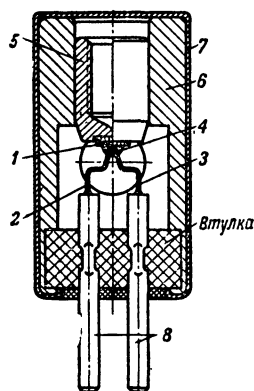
Устройство точечных триодов типов С1 и С2. 1 — германий; 2 — эмиттер; 3 — коллектор; 4 — держатель; 5 — стеклянный изолятор; 6 — корпус; 7 — кожух; 8 — вывод.
